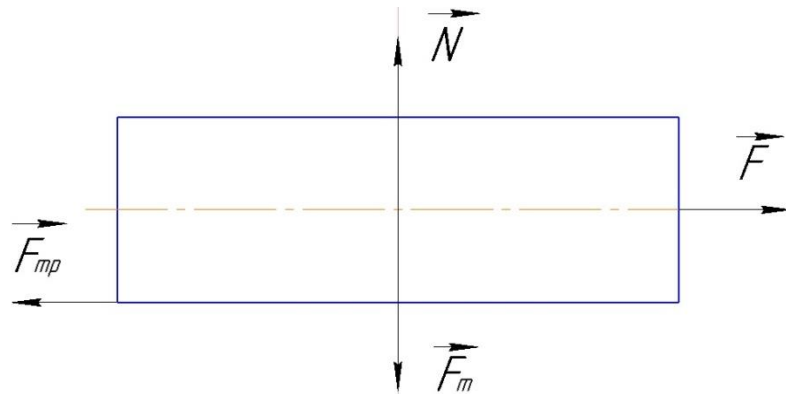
Эскиз заготовки с расставленными на нем силами, действующими на заготовку.
